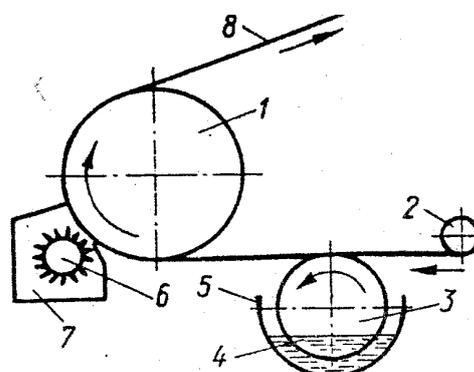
Схема устройства для нанесения покровного слоя с помощью вала и разравнивающей цилиндрической щетки:
